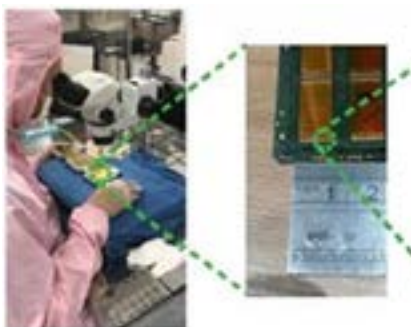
Inspeção visual convencional no processo de soldagem de pastilhas de silício
